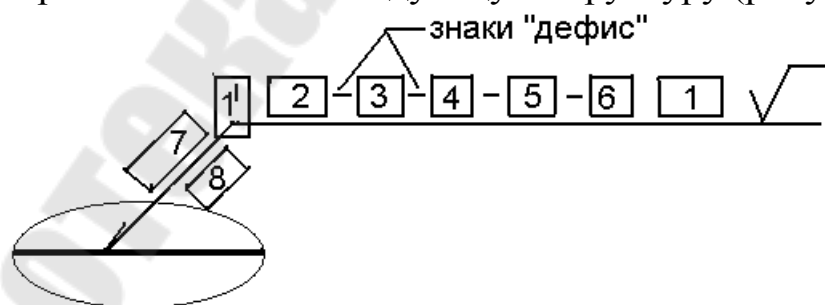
Структура условного обозначения стандартного сварного шва
